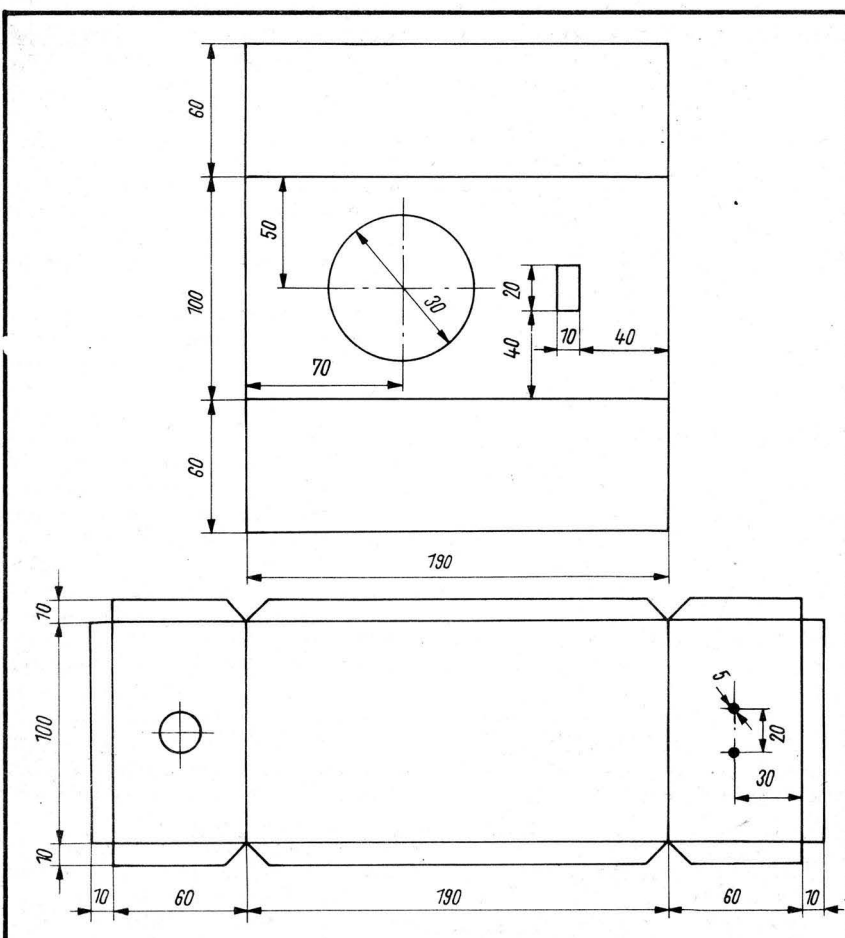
Maßskizze für das Gehäuse des Drehzahlmessers
